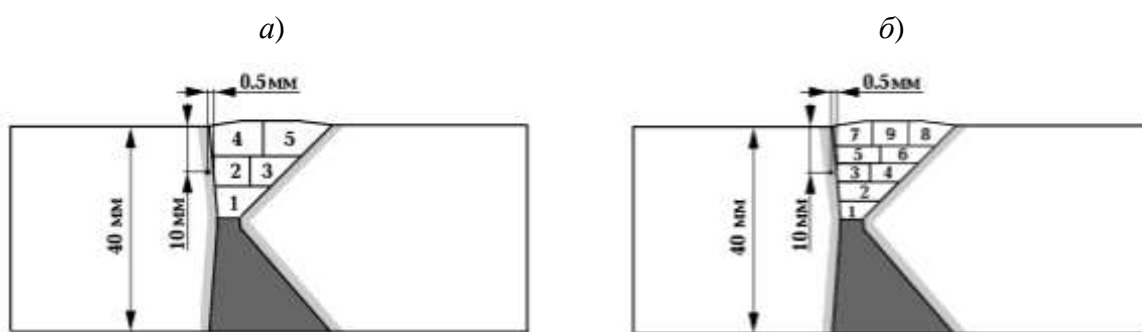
Раскладка валиков в модели сварного соединения для стороны, свариваемой последней. Указано расположение расчётной точки.
